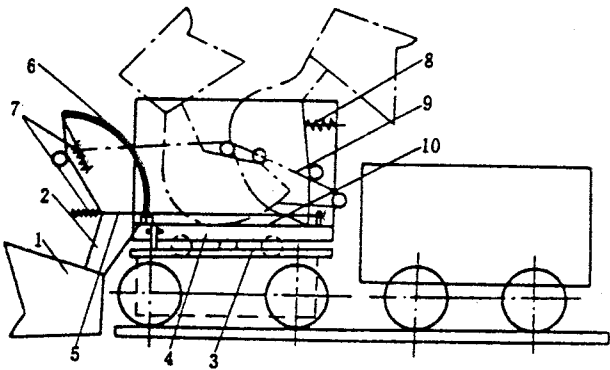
3 - 8 H - 600 型装岩机结构示意图
